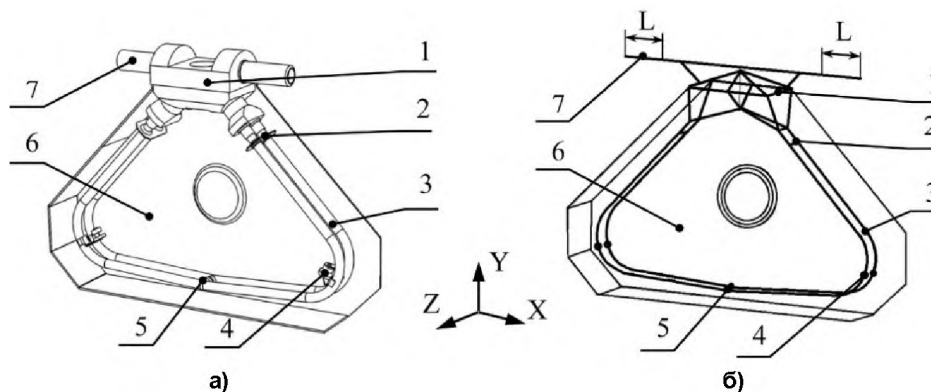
Схема (а) и расчетная модель (б) системы «расходомер – трубопроводы»: 1 – основание (BEAM188); 2 – переключки (BEAM188); 3 – трубки (BEAM188); 4 – измерительные катушки (MASS21); 5 – задающая катушка (MASS21); 6 – корпус (SHELL181); 7 – трубопроводы (BEAM188)
